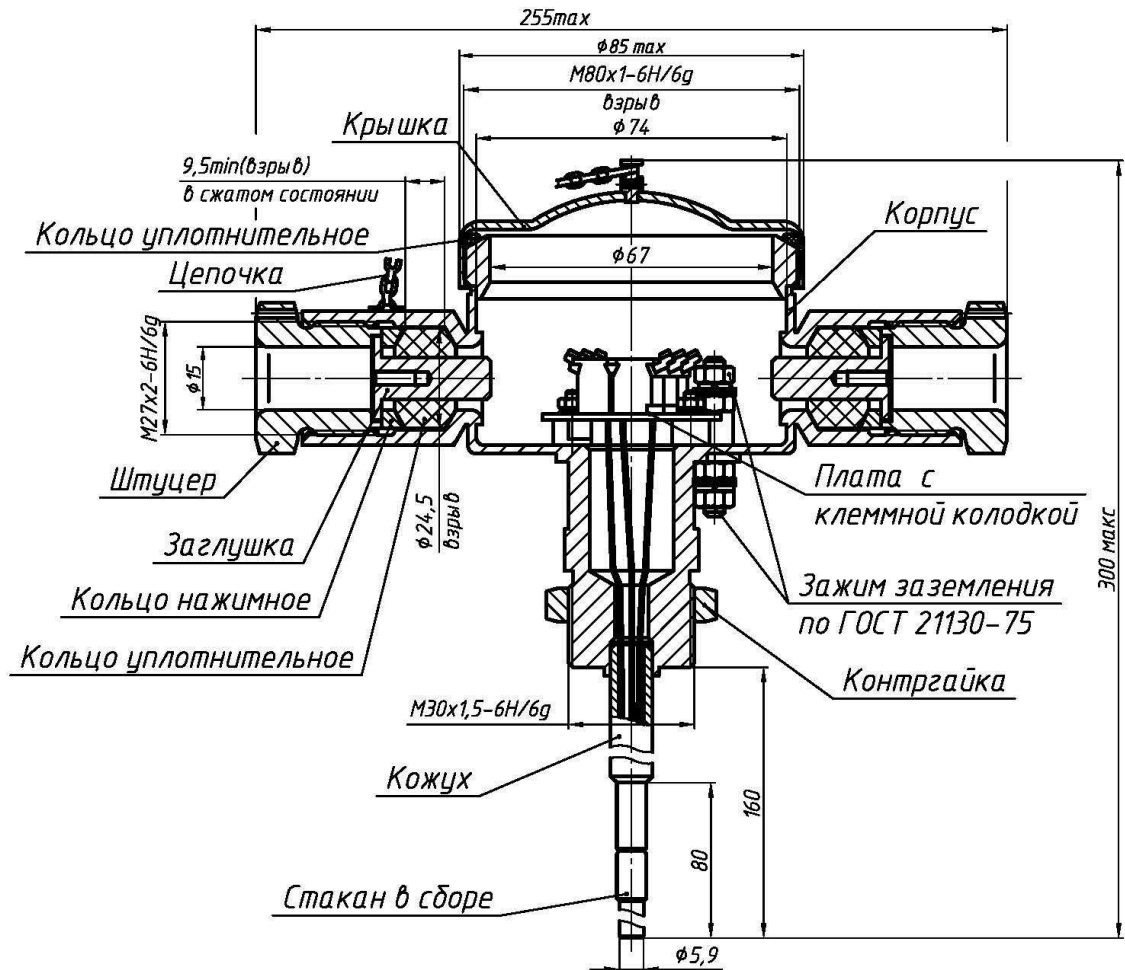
Габаритный чертёж ИП103-2В/П-А в алюминиевом корпусе (вариант)
